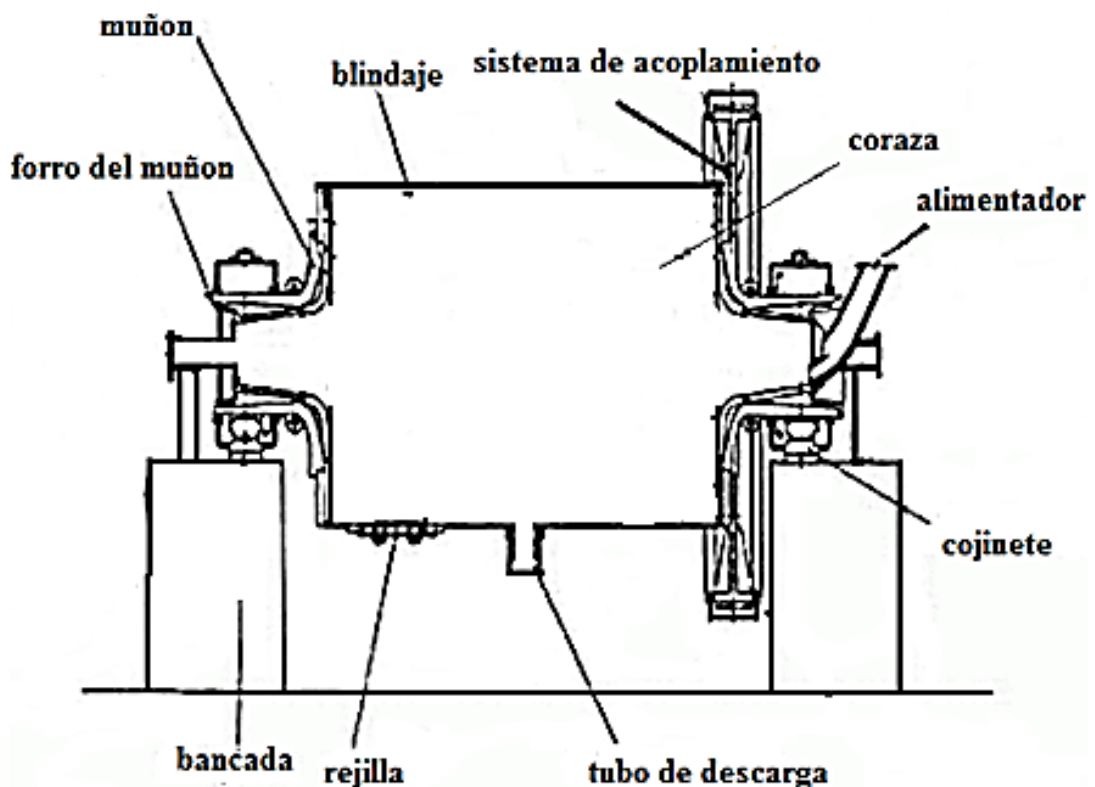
3: PARTES DEL MOLINO DE TAMBOR DE BOLAS. FUENTE: AUTOR
